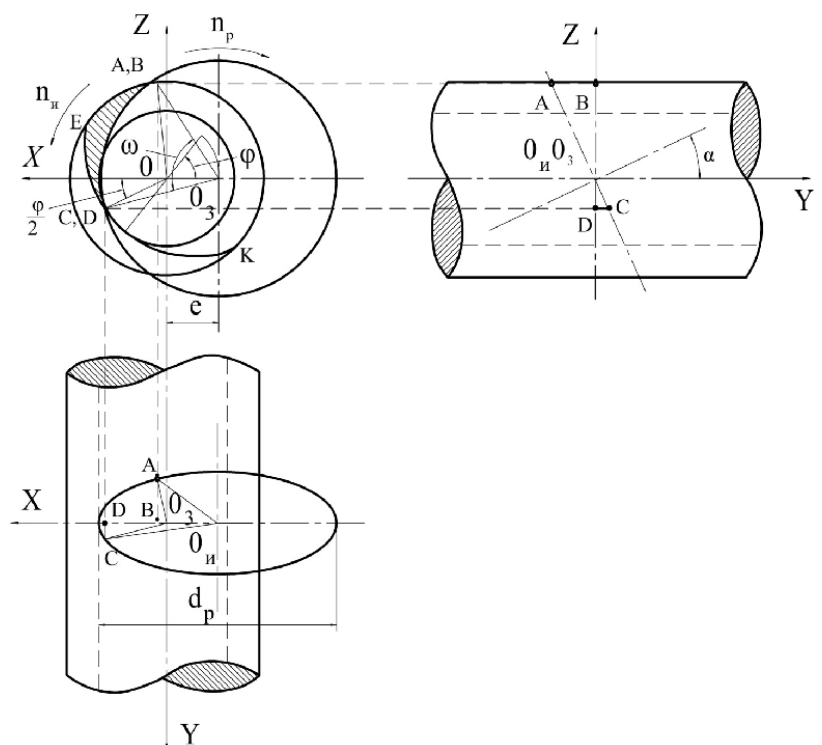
Схема определения угла поворота заготовки между двумя касаниями резца
